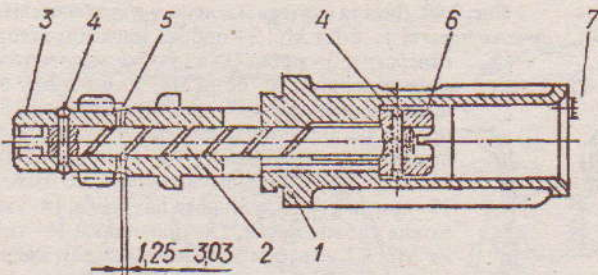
Привод распределителя зажигания: 1 - корпус привода валика распределителя зажигания; 2 - валик привода распределителя зажигания; 3 - шестерня привода распределителя зажигания; 4 - штифт; 5 - шайба упорная; 6 - привод распределителя; 7 - шпилька
